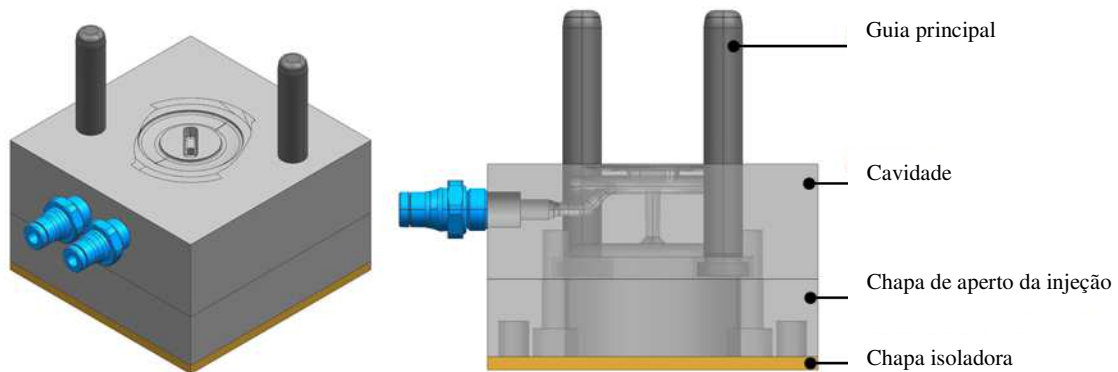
Lado da injeção do molde de fabrico aditivo, *Sensor housing
